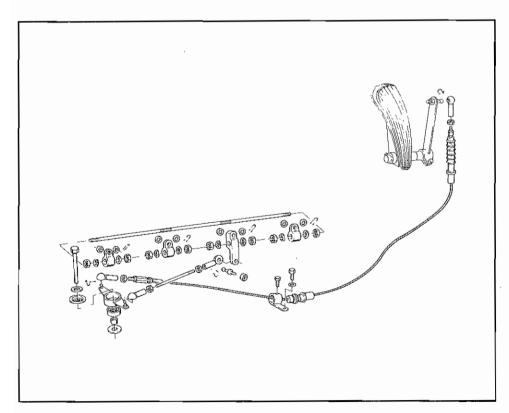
Leveraggio comando carburatori cambio meccanico Control lever assy for gearbox carburettors
